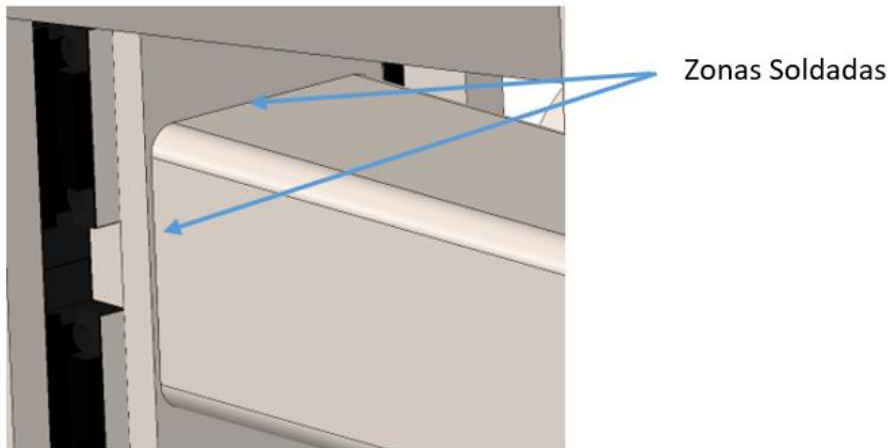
Zona de soldadura entre o bloco central e o tubo de seção quadrada
